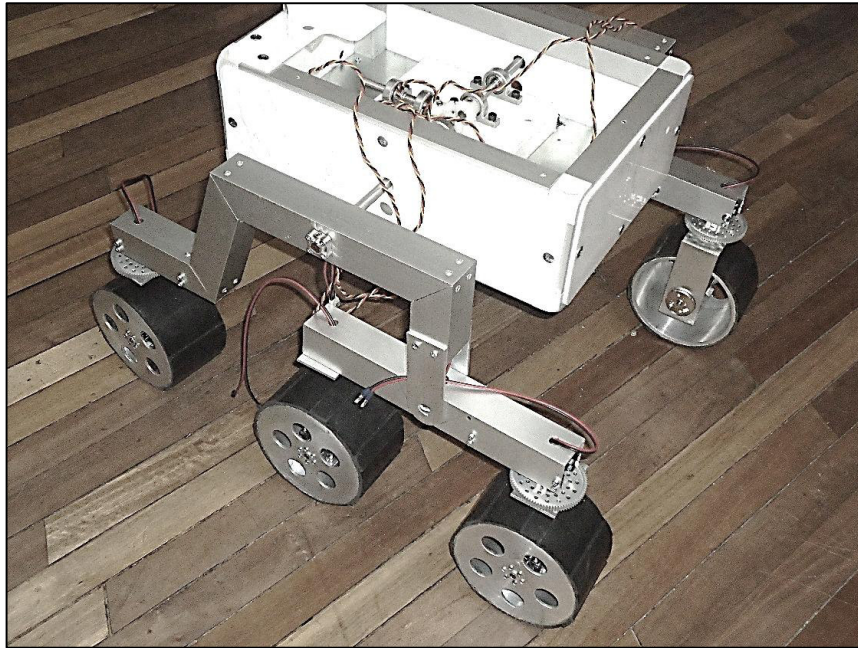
Resultado final del ensamblaje mecánico del robot.
